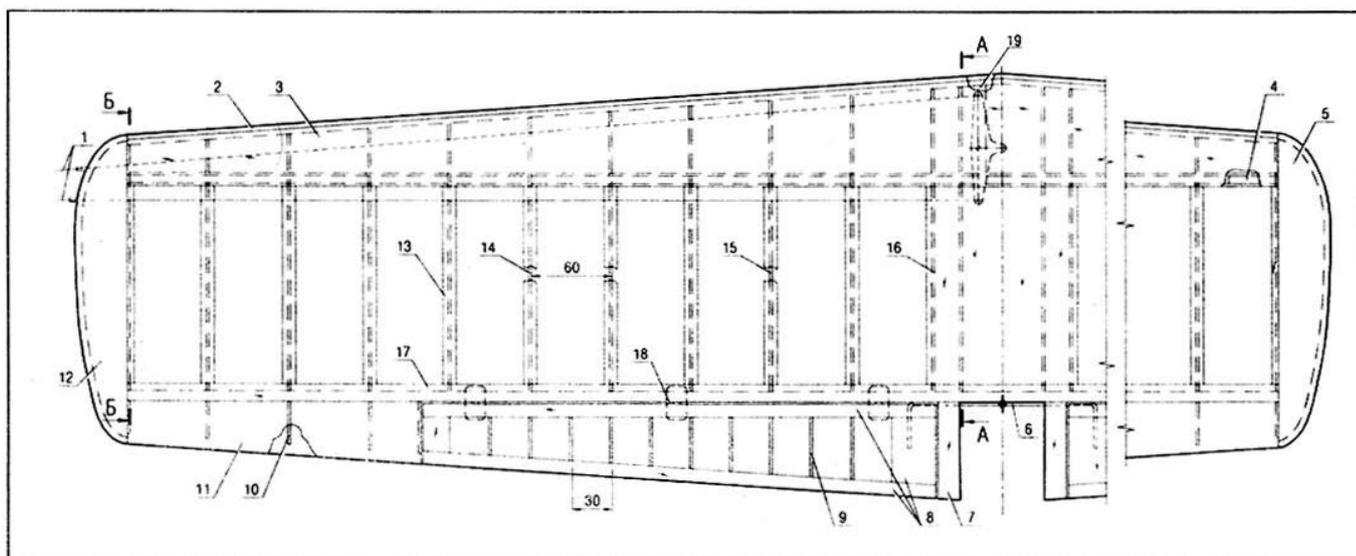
Чертёж крыла кордовой модели F-2-B
